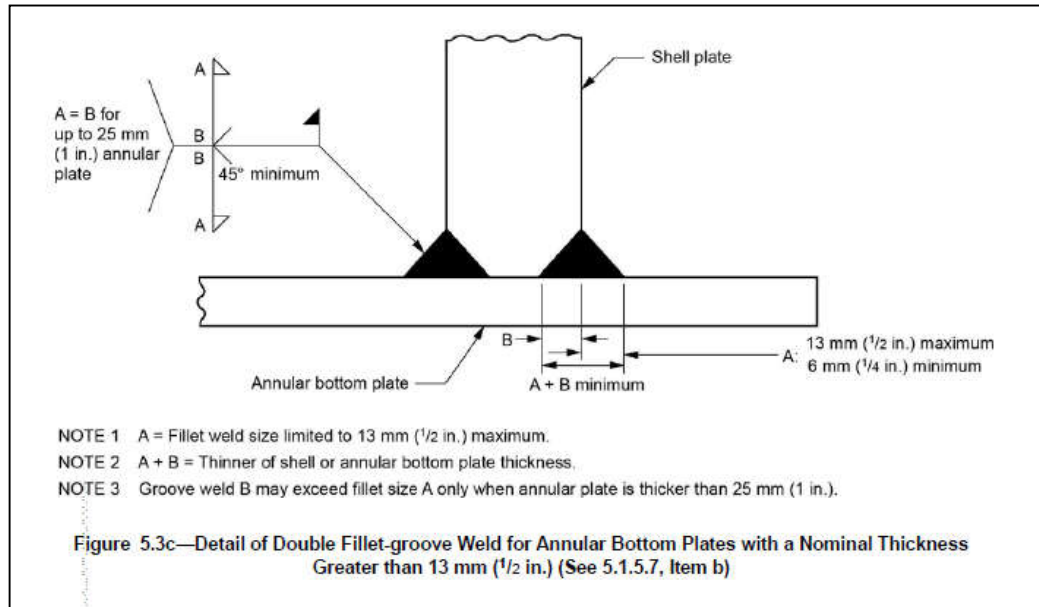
Detalle de soldadura de carcasa con fondo Tomada de API 650 (5)
